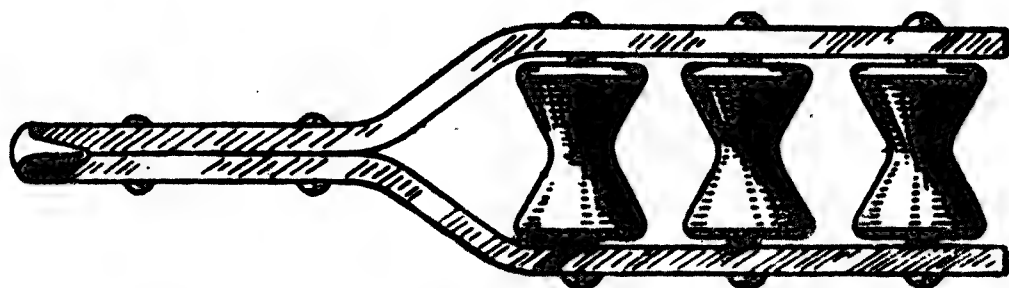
Ролики для натяжения бандажей проволоки.
